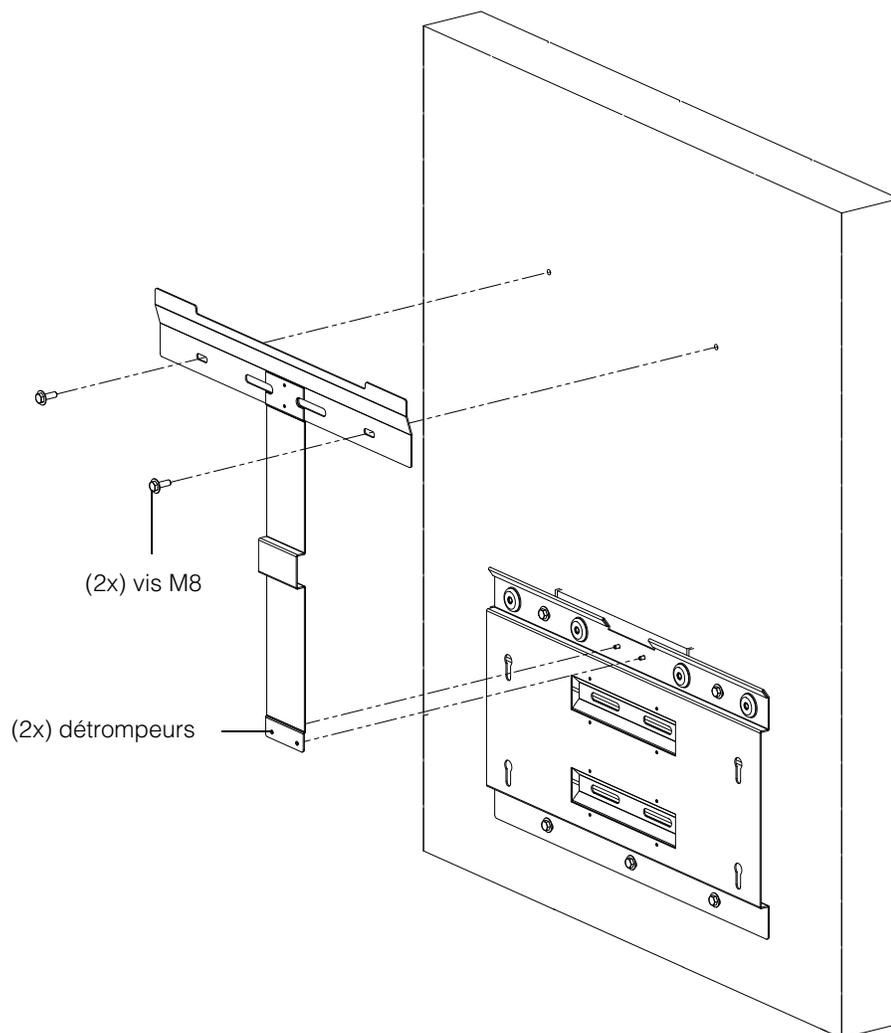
Fixation au mur du support de montage de l'onduleur
